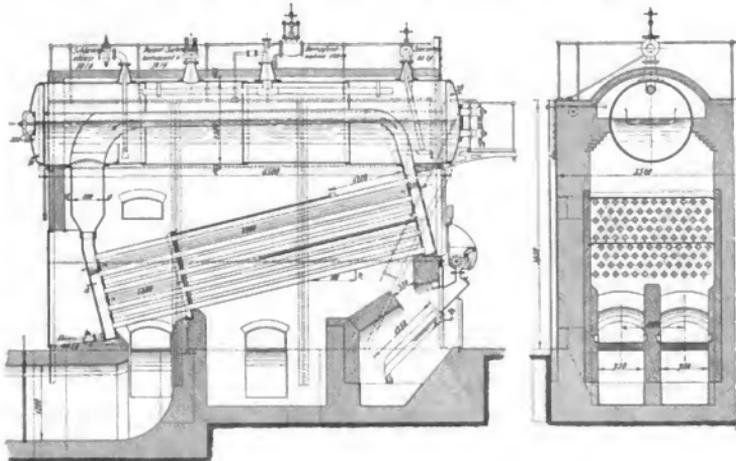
Wasserrohr-Schnellumlaufkessel von A. Büttner & Co.
